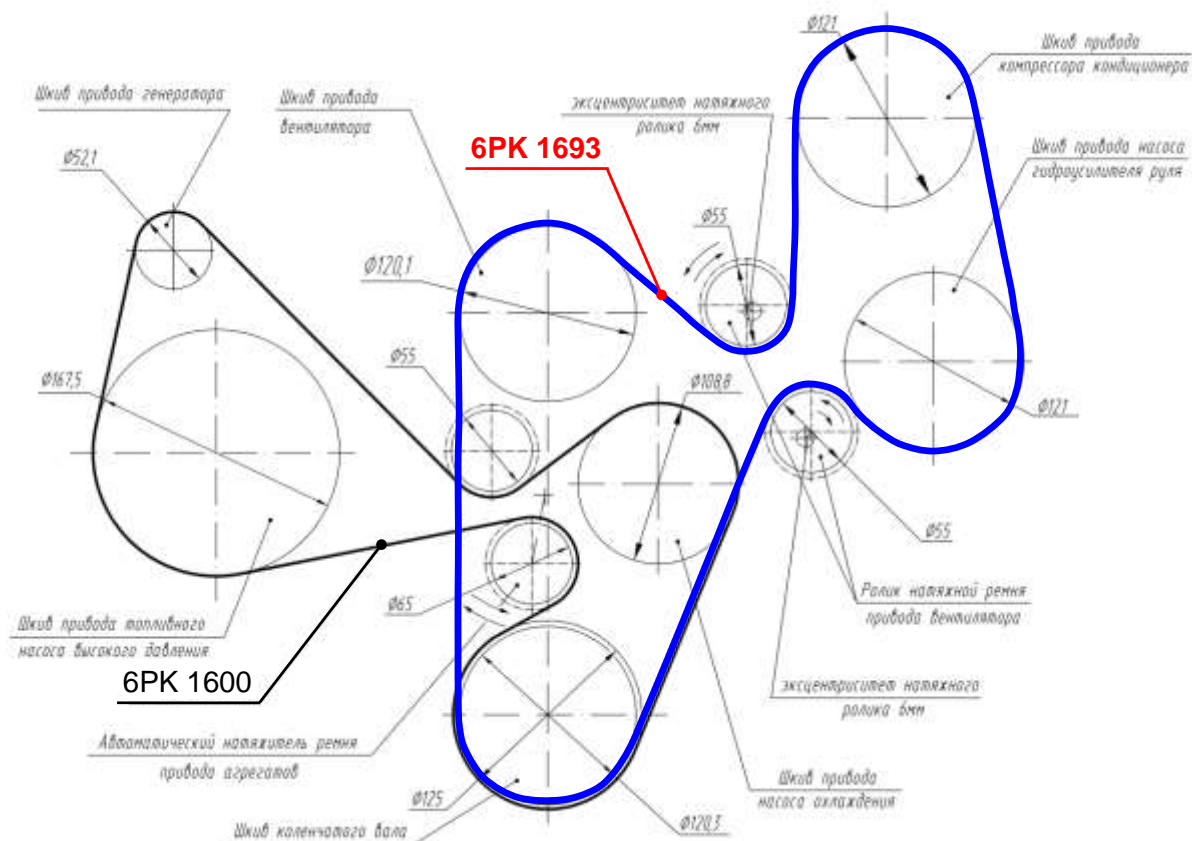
Схема привода вспомогательных агрегатов двигателя для автомобилей на платформе УАЗ-3163 с компрессором кондиционера
